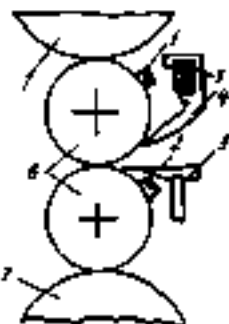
Схема расположения устройств для подачи смазки на стане 2800:
